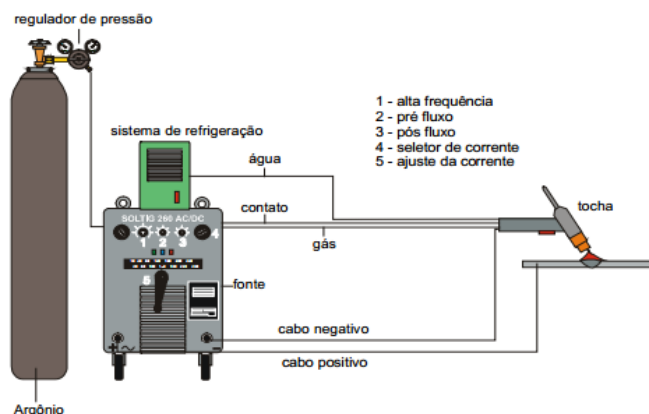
Esquema dos equipamentos básicos para soldagem TIG
